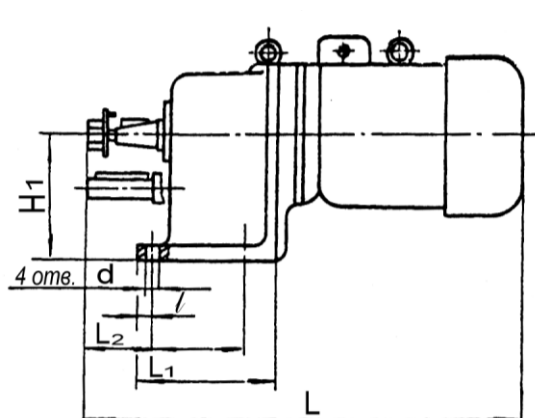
П6 Габаритные и присоединительные размеры мотор-редуктора на лапах
